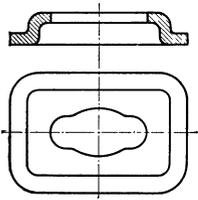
Schnittplatte aus hohigepreßtem Werkzeugstahlblech.
